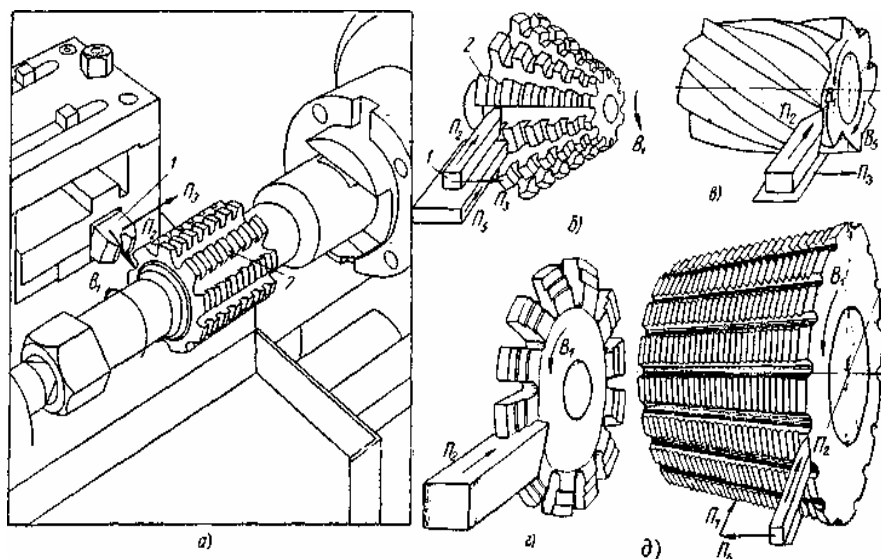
Схемы движений инструмента и заготовки при затыловании фрез: а – червячной; б – червячной конической; в – цилиндрической с винтовым зубом; г – дисковой; д – гребенчатой резьбовой
